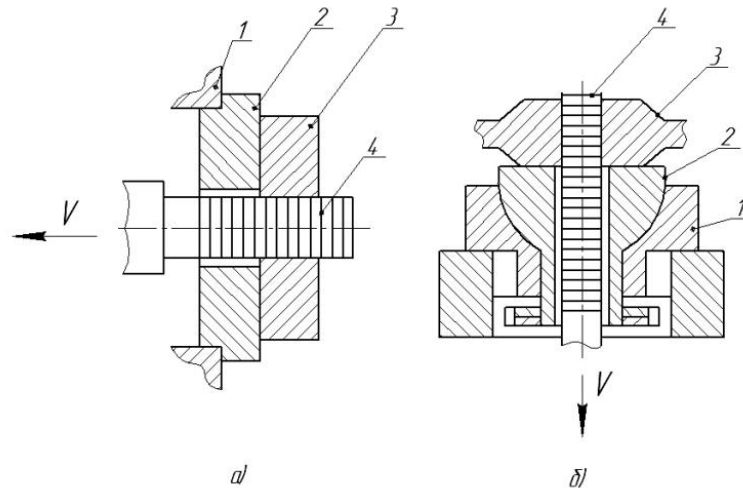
Схеми протягування отворів: а – горизонтальна; б – вертикальна; 1 – жорстка опора; 2 – шарова опора; 3 – оброблювальна заготовка; 4 – протяжка
